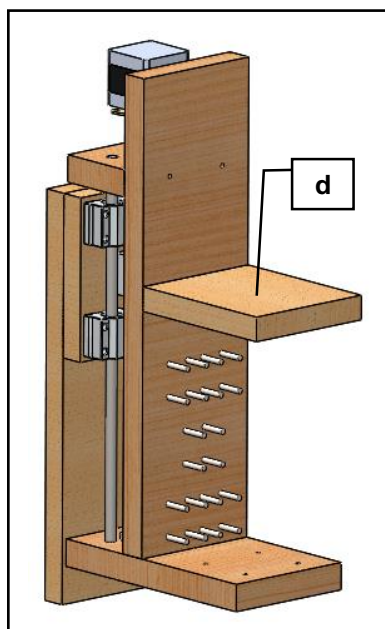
Ensamble de la pieza Z1 a la estructura eje Z
